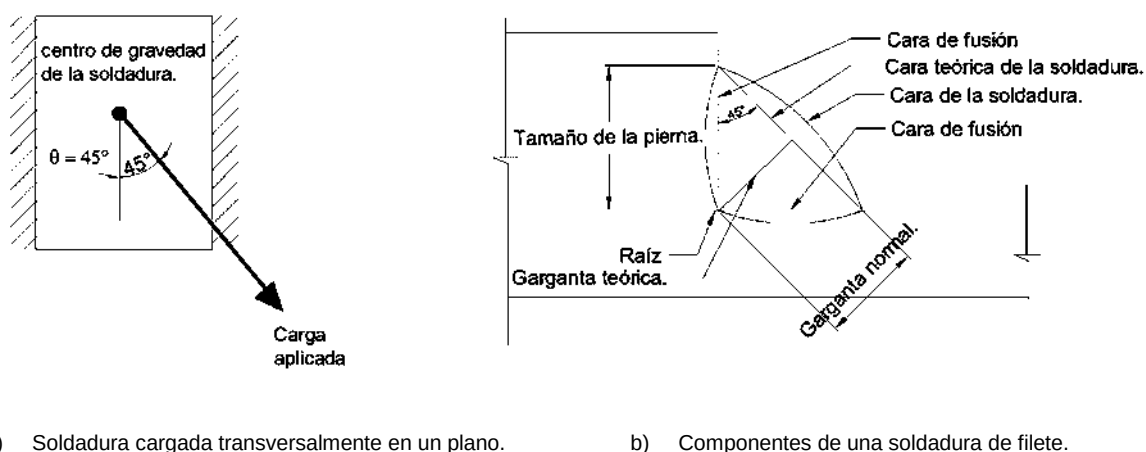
11 Soldadura cargada transversalmente y componentes de una soldadura (Modificado de Jack, C. & Stephen, F. 2012).
